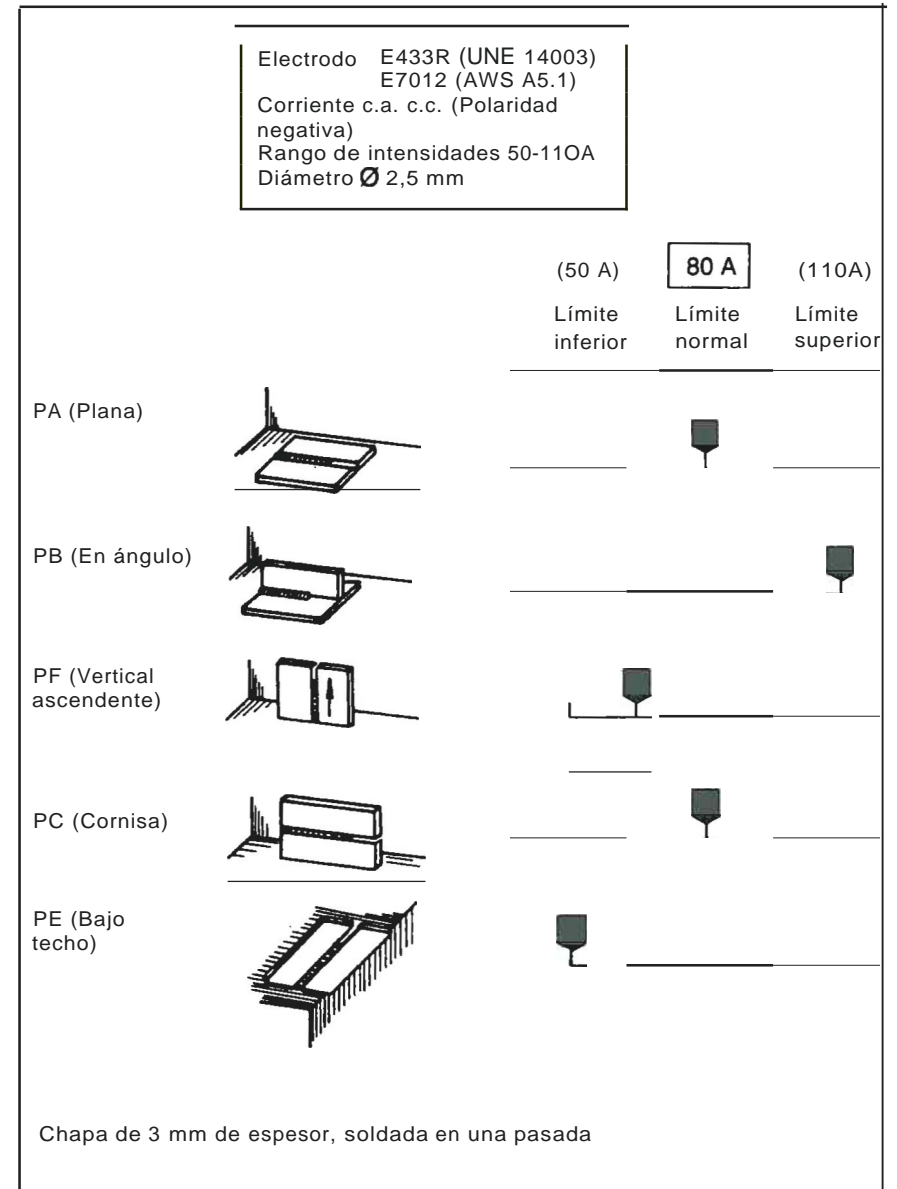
INTENSIDAD DE SOLDEO EN FUNCIÓN DE LA POSICIÓN
